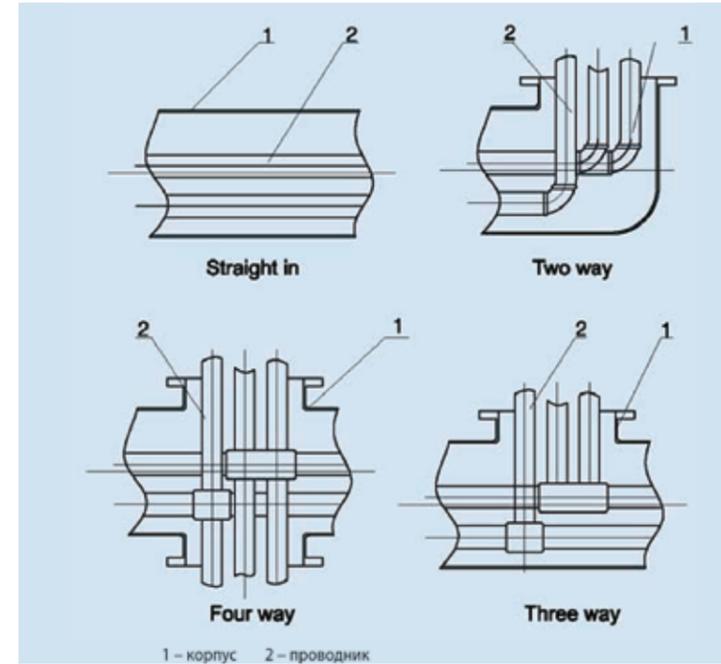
Схема конструкции трехфазной шины с отводами обычного барабанного типа
